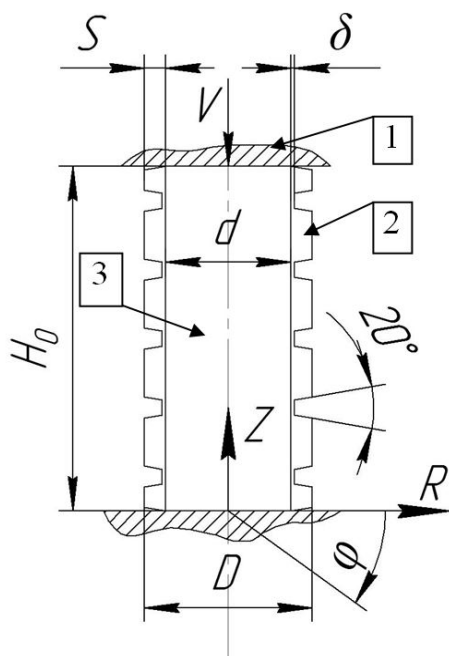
Схема осадки заготовки цилиндрической формы в комбинированной оболочке (бандаже): 1 – плоские бойки, 2 – бандаж с кольцевыми проточками, 3 – заготовка цилиндрической формы. Буквенные обозначения: H_0 – начальная высота заготовки; D – диаметр бандажа; d – диаметр цилиндрической заготовки; V – скорость осадки; S – ширина бандажной стенки; δ – толщина перемычки между соседними кольцами бандажа; Z, R, φ – полярные координаты.
